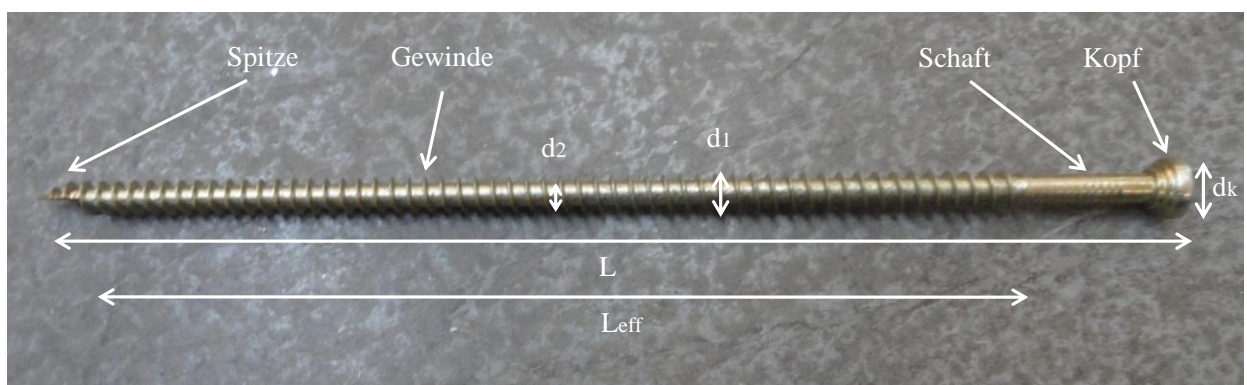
Schraubenbezeichnung und Schraubengeometrie
